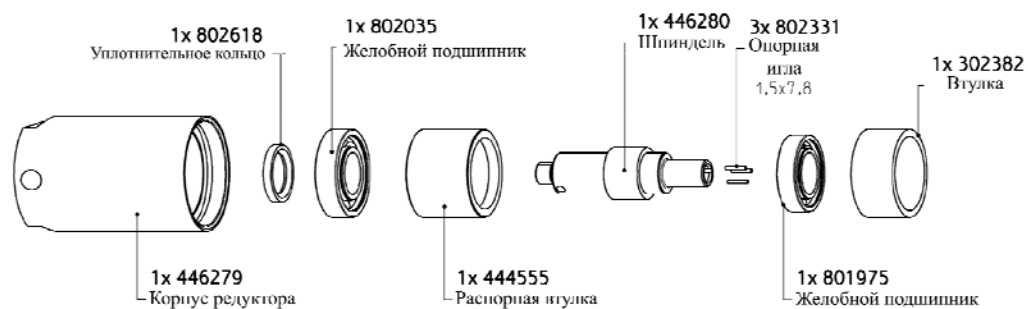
Детализовка пневматического двигателя JP-AIR 2.
